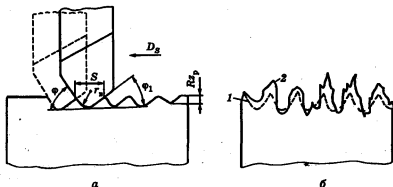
Схема образования шероховатости поверхности: а — образование регулярного профиля шероховатости; б — его искажение за счет пластической деформации в зоне резания; 1, 2 — соответственно регулярный и искаженный (действительный) профили
